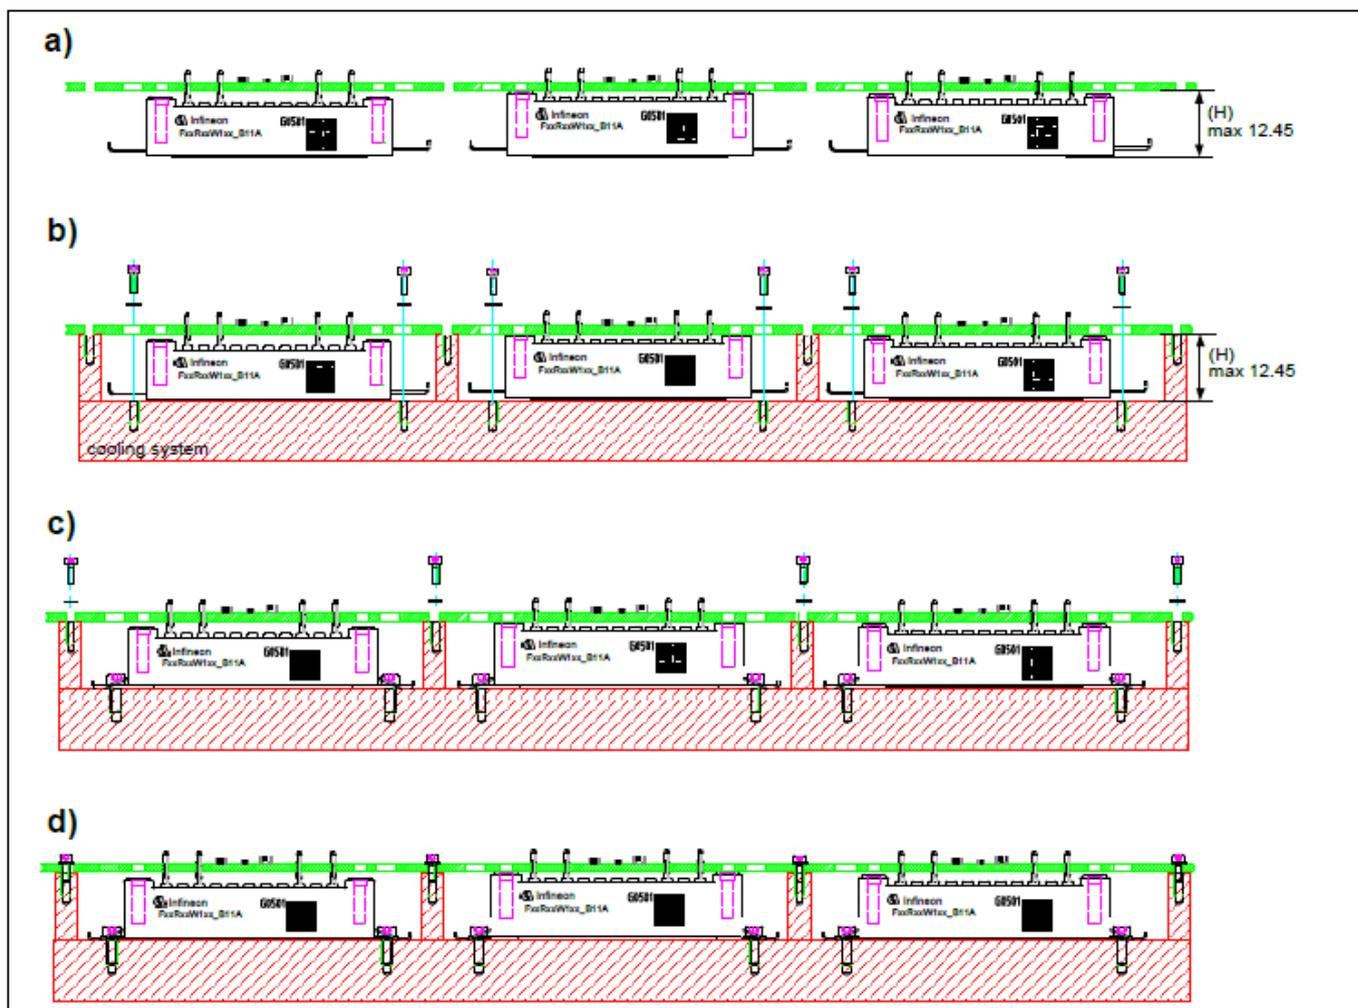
PCB 和模块安装到冷却系统 (图纸不符合比例)
